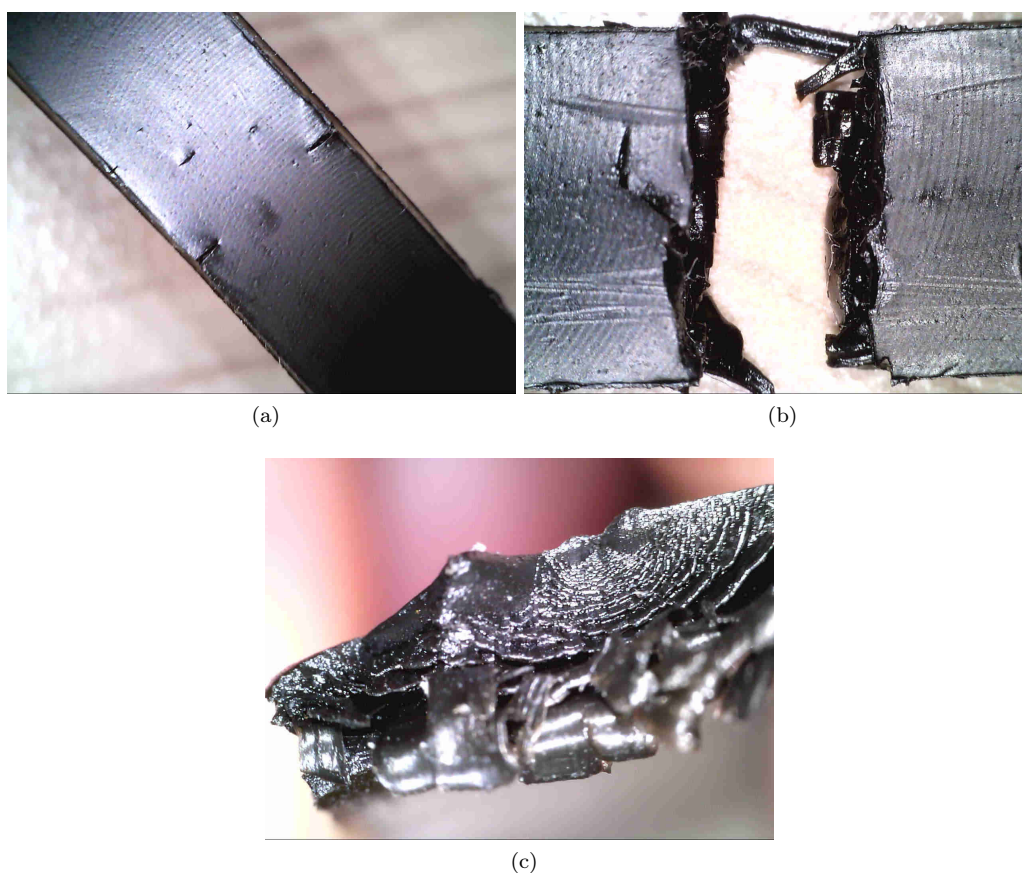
Faciès de rupture en fatigue d'éprouvettes obtenues par le procédé d'extrusion-soufflage
